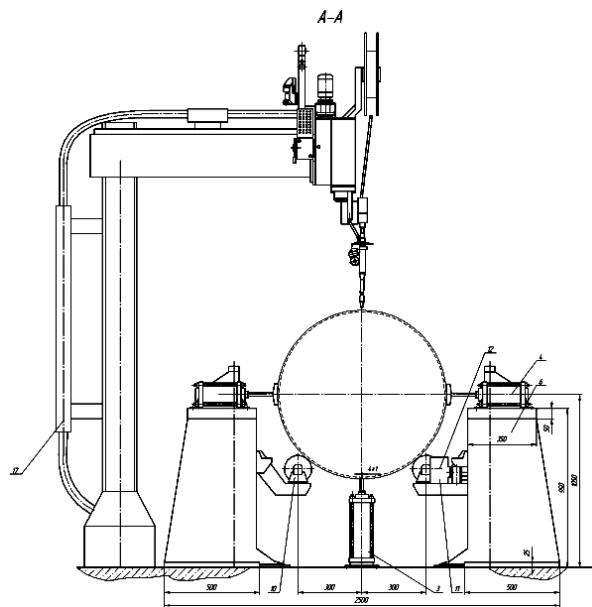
Установка для полного складання і автоматичного зварювання обичайки цистерни
